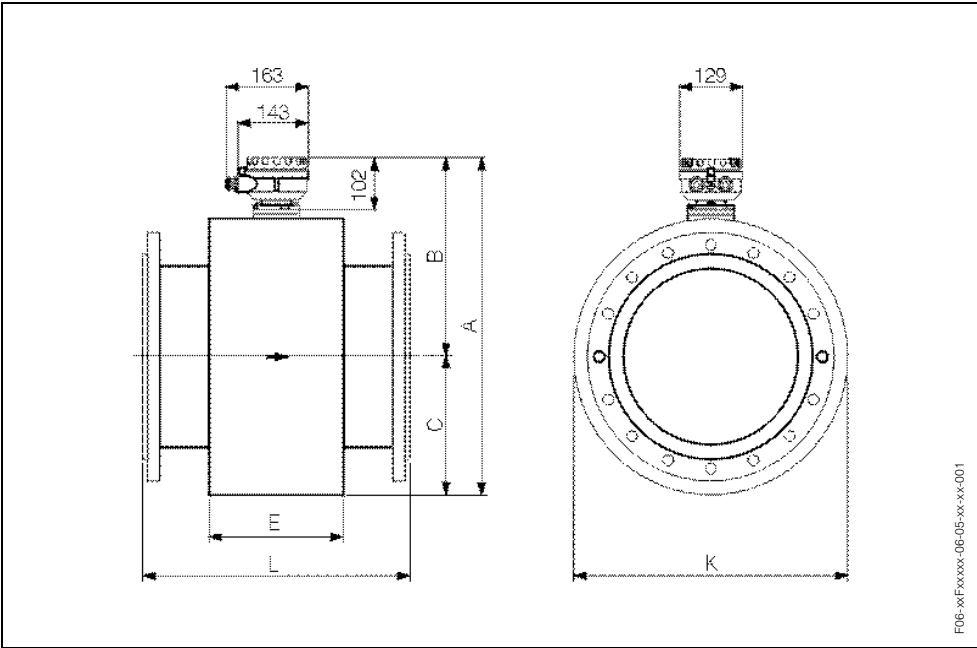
Dimensiones Promag P / DN ≥ 350 (versión separada)
